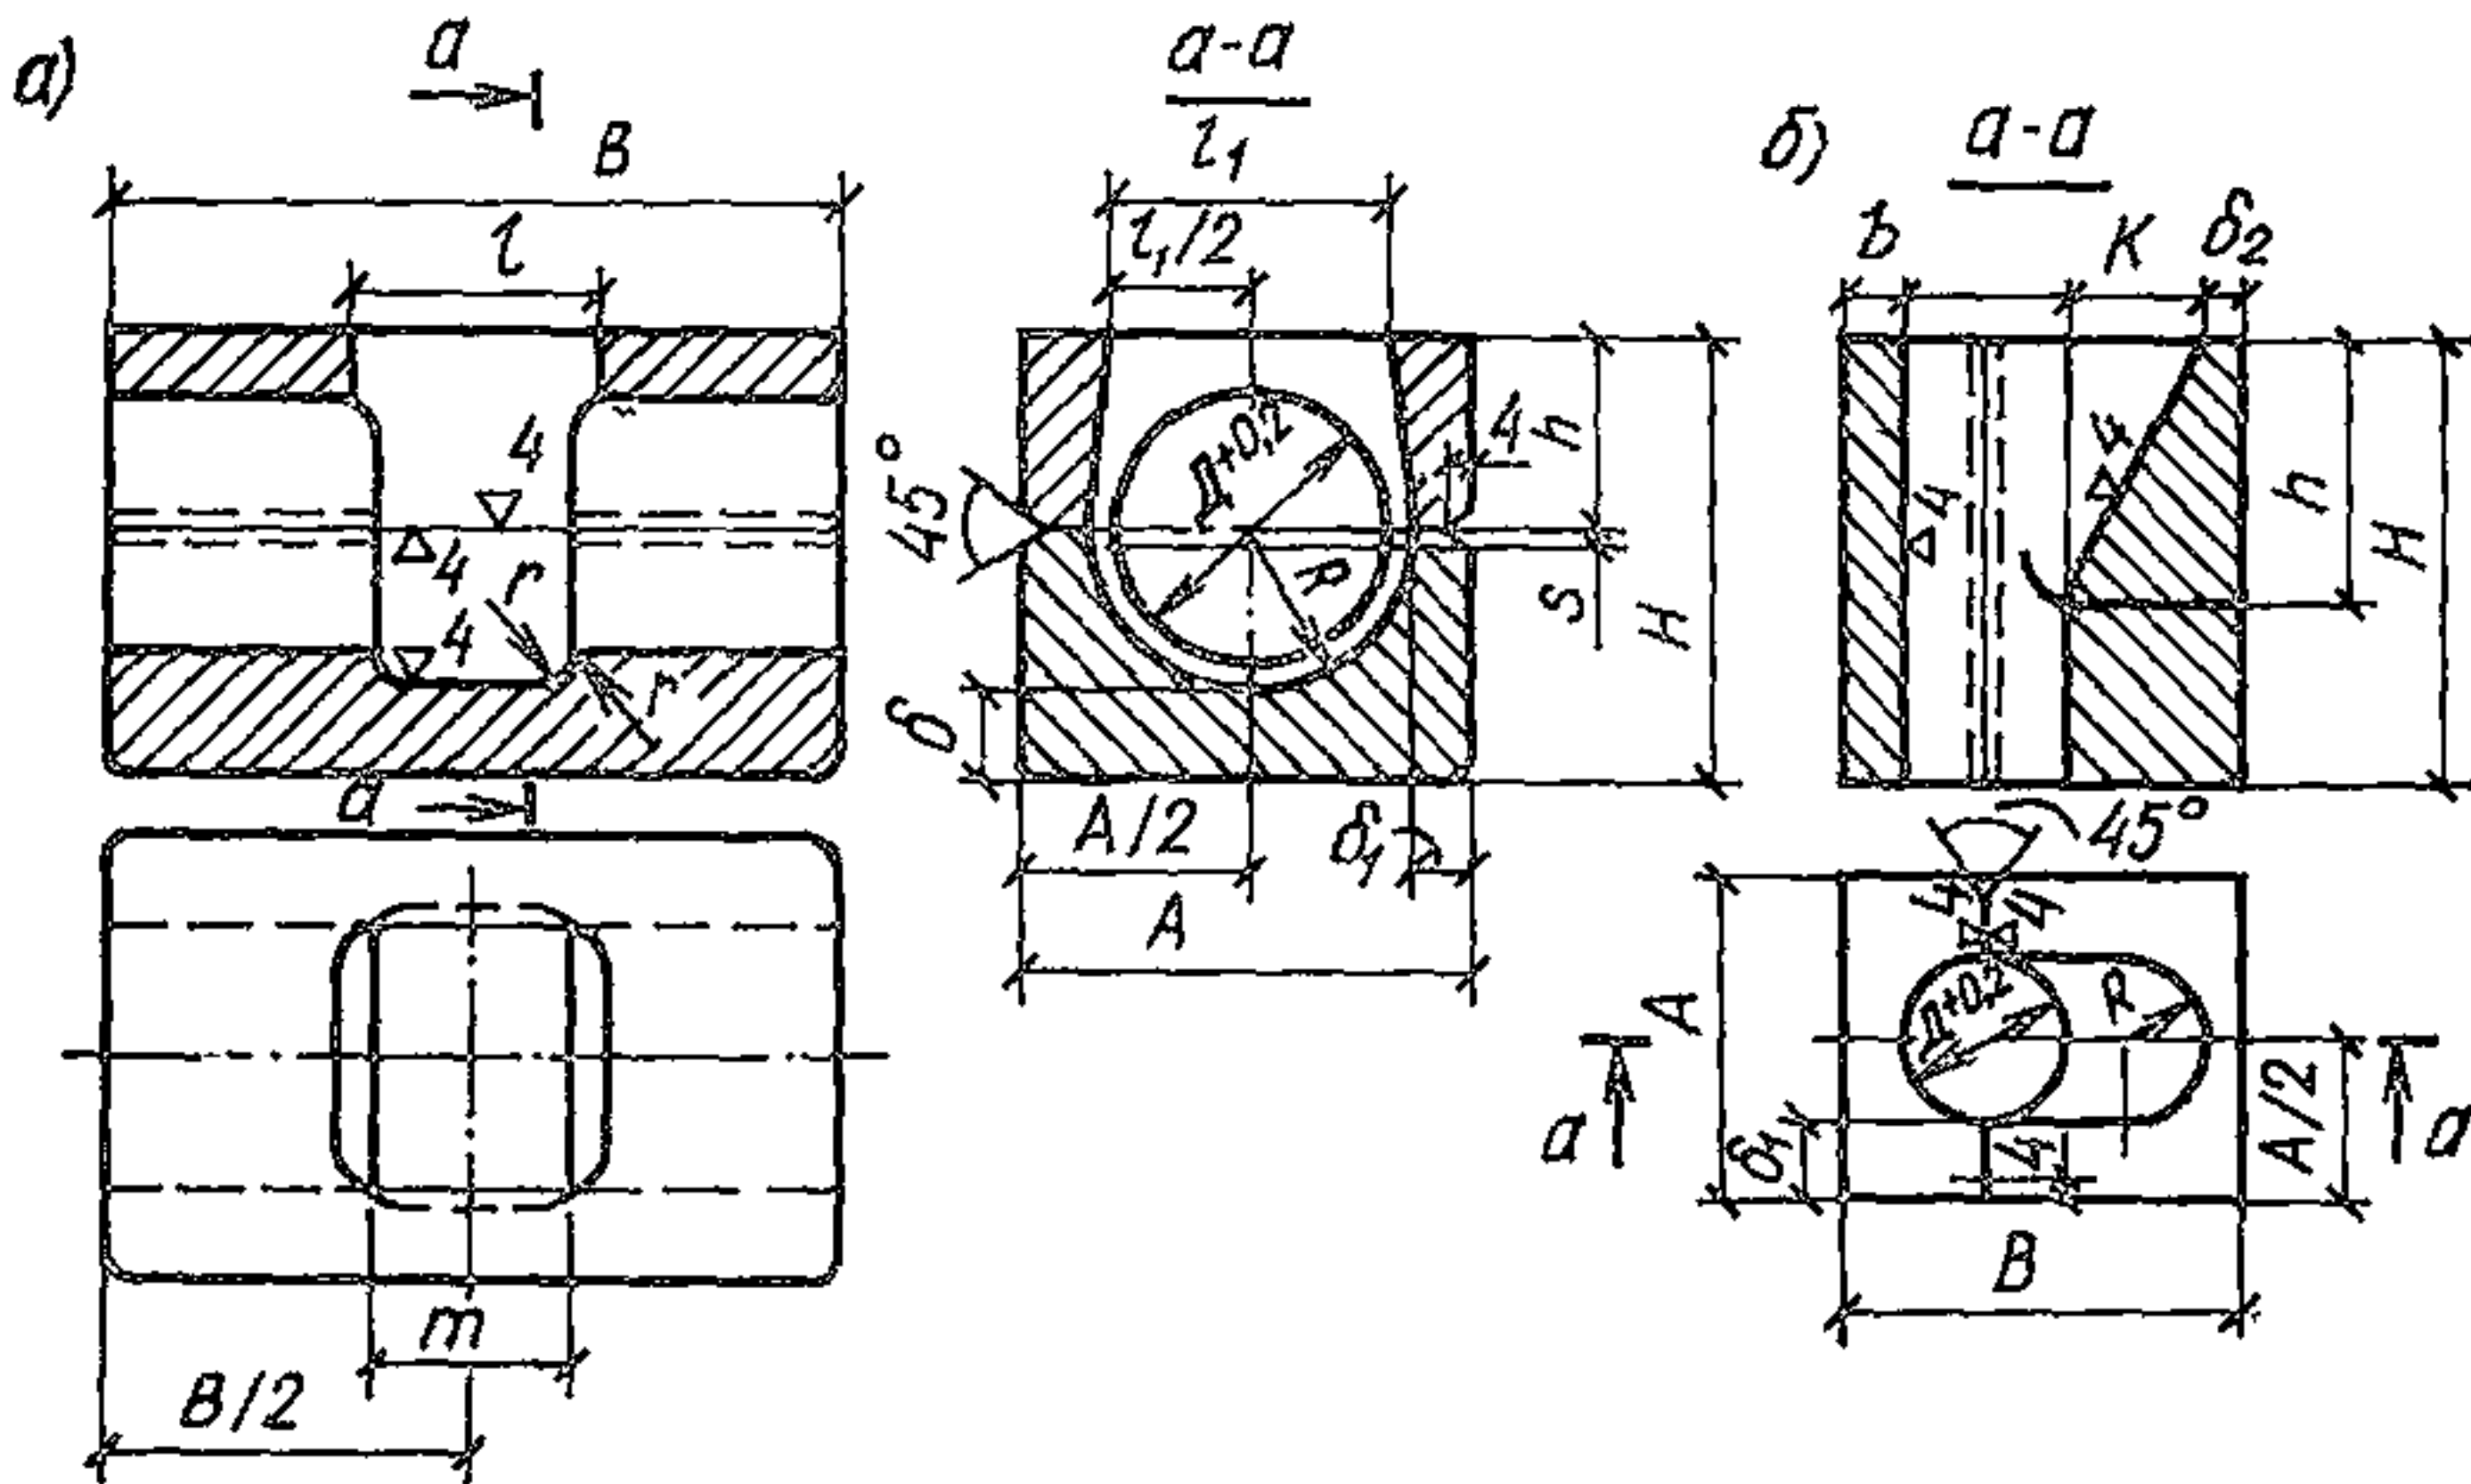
Конструкция призматических инвентарных медных форм для ванной сварки стыковых соединений однорядных стержней
